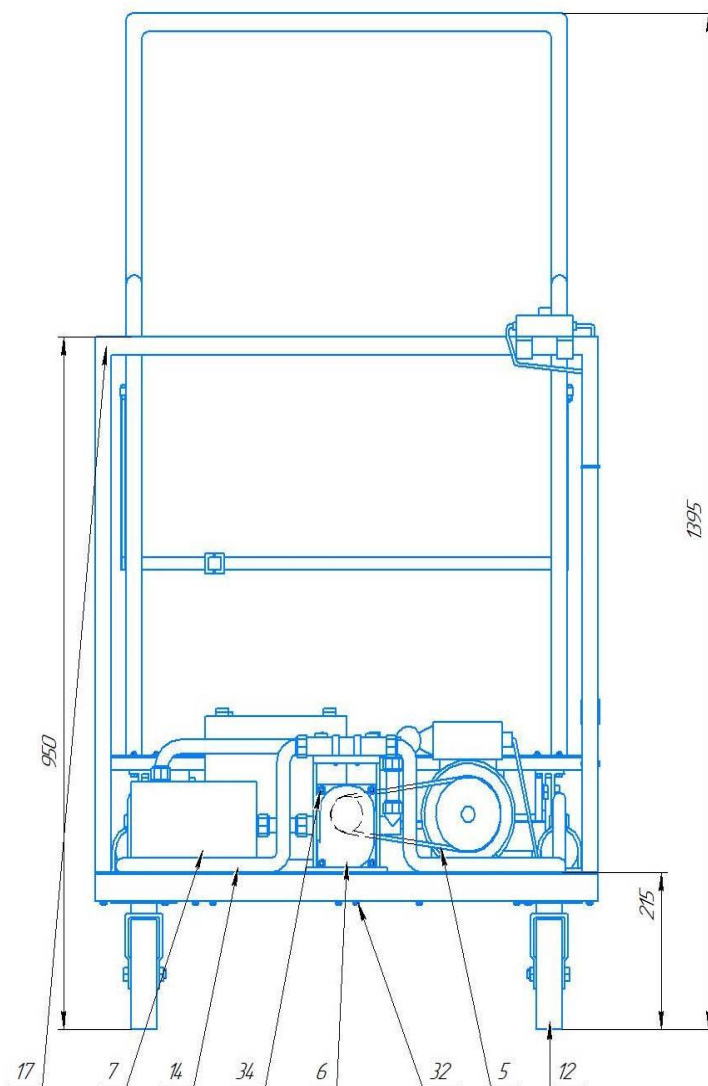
Схема разрабатываемого образца (вид сбоку)
